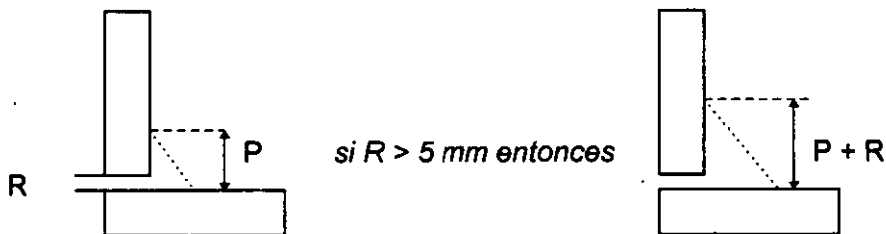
Abertura de raíz para soldaduras de filete.
